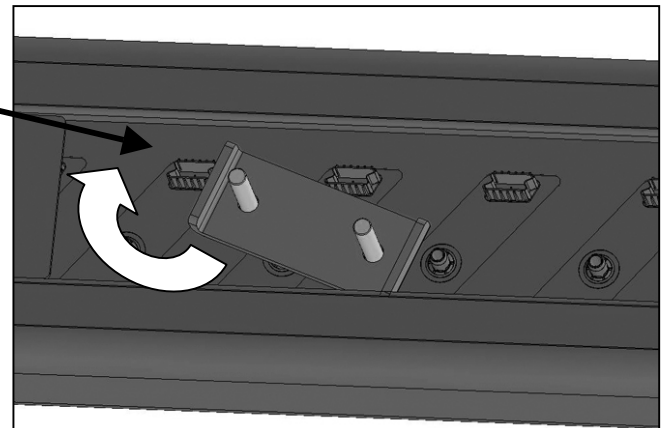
Soporte frontal izquierdo/del lado del conductor instalado
